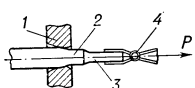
Схема волочения: 1 — волока; 2 — заготовка; 3 — заостренный конец заготовки; 4 — захват.
